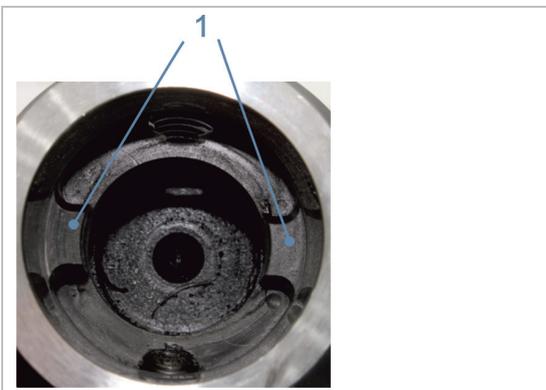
HSK-Mitnehmer der Maschinenspindel
